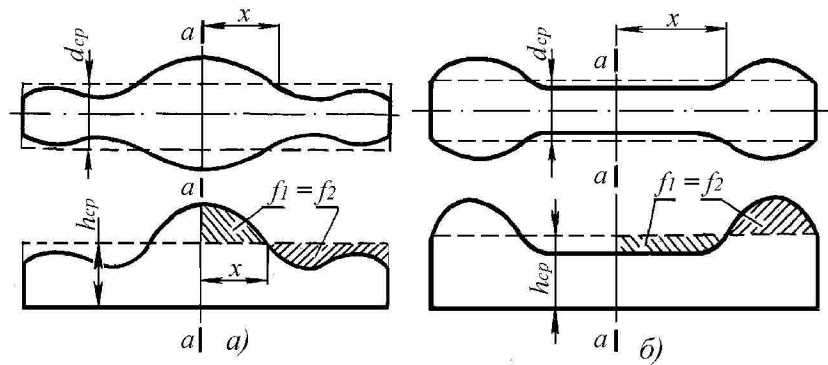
Схема приведення складних розрахункових заготовок до двох елементарних
